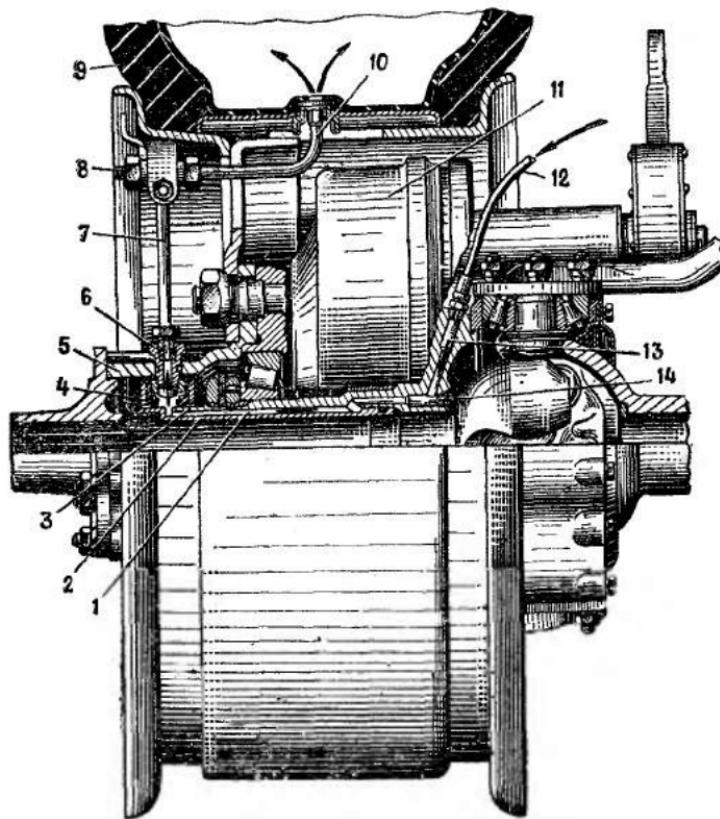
Схема подвода воздуха к шине переднего колеса:
